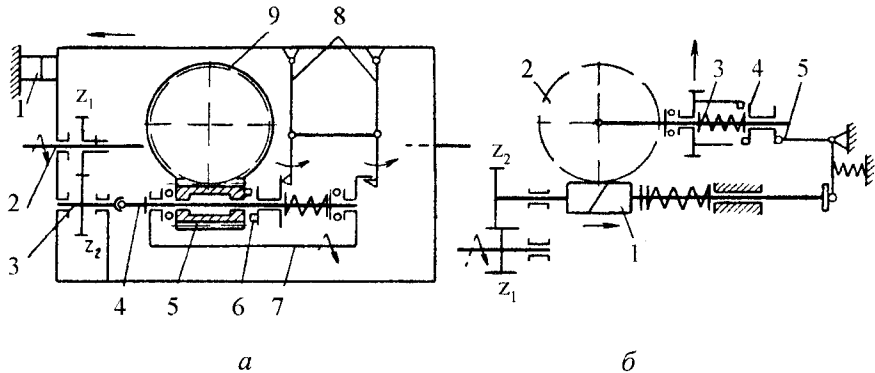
Схеми пристроїв для обмеження ходу з черв'яком:
